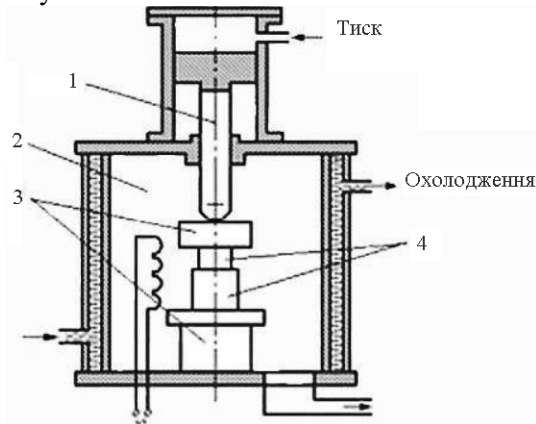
Схема дифузійного зварювання: 1 – силовий механізм; 2 – робоча камера; 3 – оправка; 4 – матеріал, що зварюється
